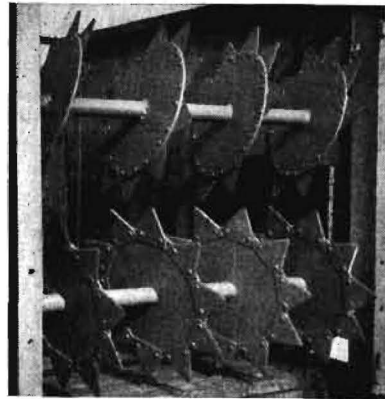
Schräggestehende Scheiben mit Mähmessenklingen als Dosierwerkzeug
